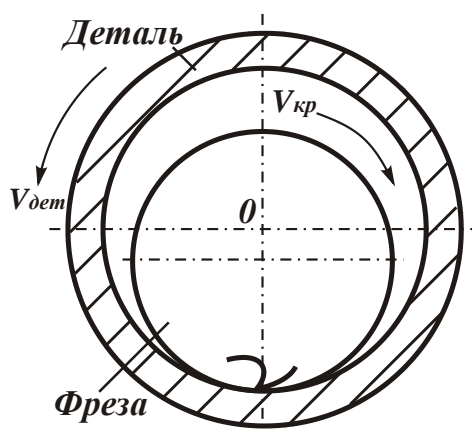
Схема фрезерування отвору кінцевою фрезою
